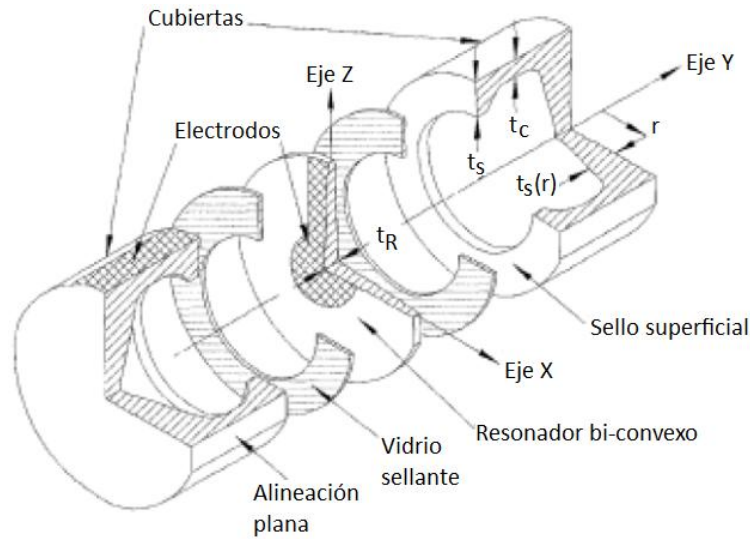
Vista isométrica de un Shear Thickness Shear Mode de presión.
